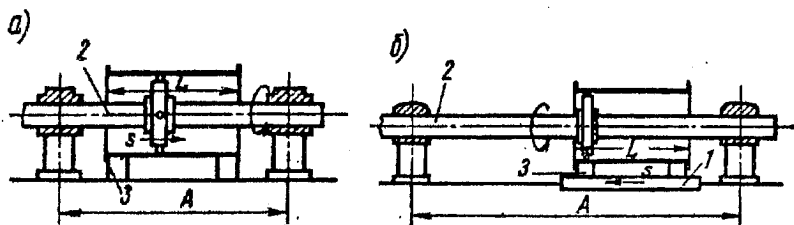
Схеми обробки на розточувальних верстатах:
